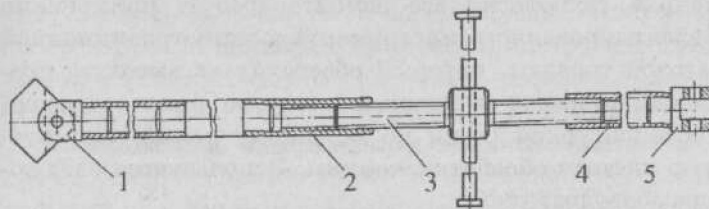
Винтовое рихтовочное приспособление с механическим приводом
